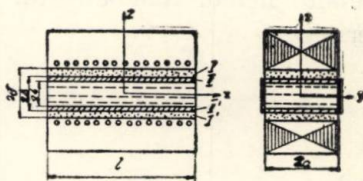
Secțiune longitudinală și transversală prin pompa liniară plană.
